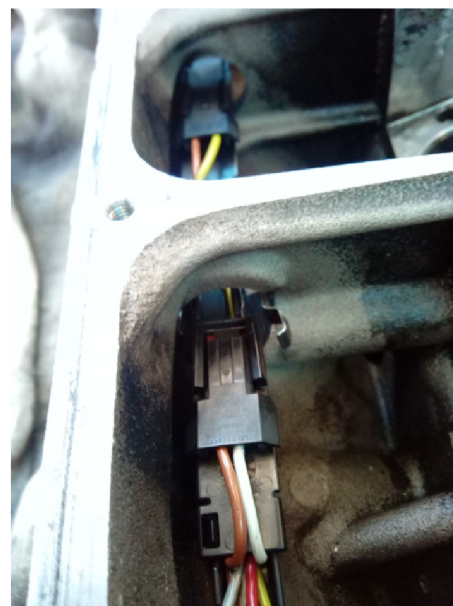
9 Dosednutí konektoru PD k bloku motoru
